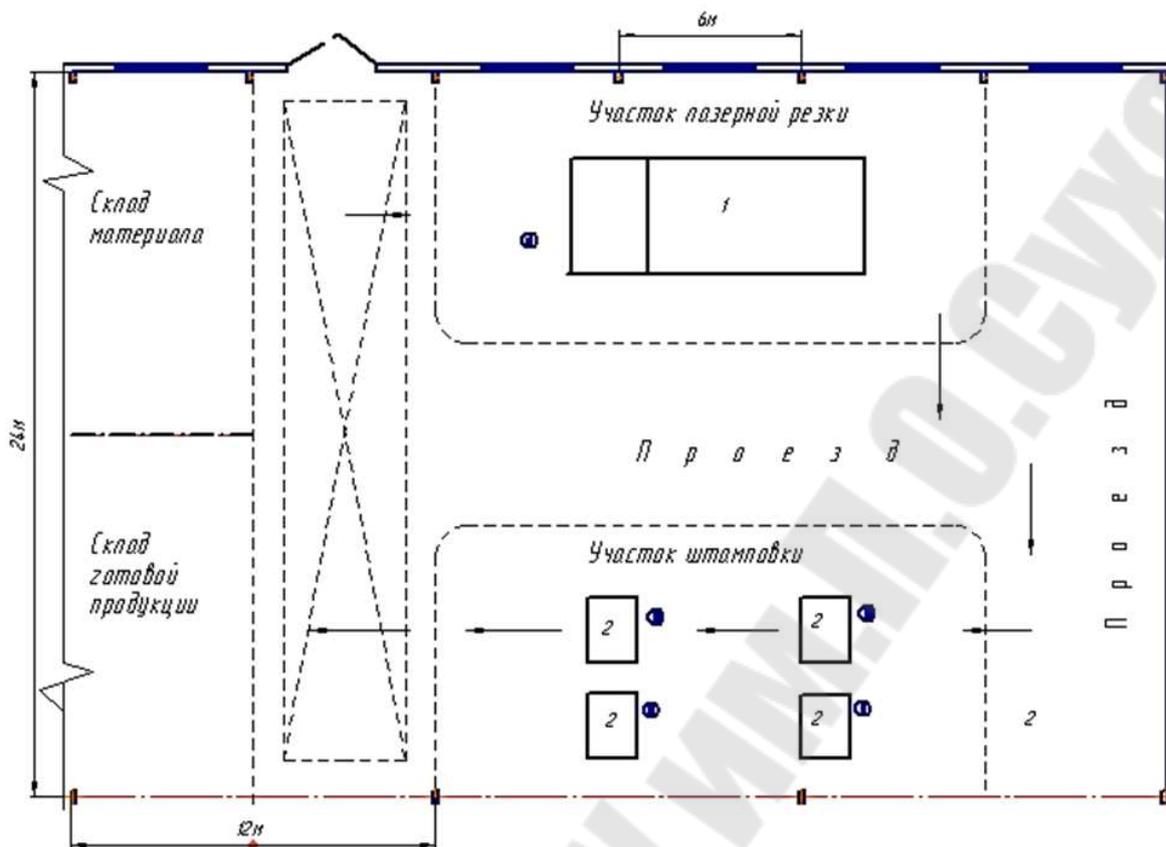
Схема фрагмента планировочного чертежа цеха листовой штамповки
